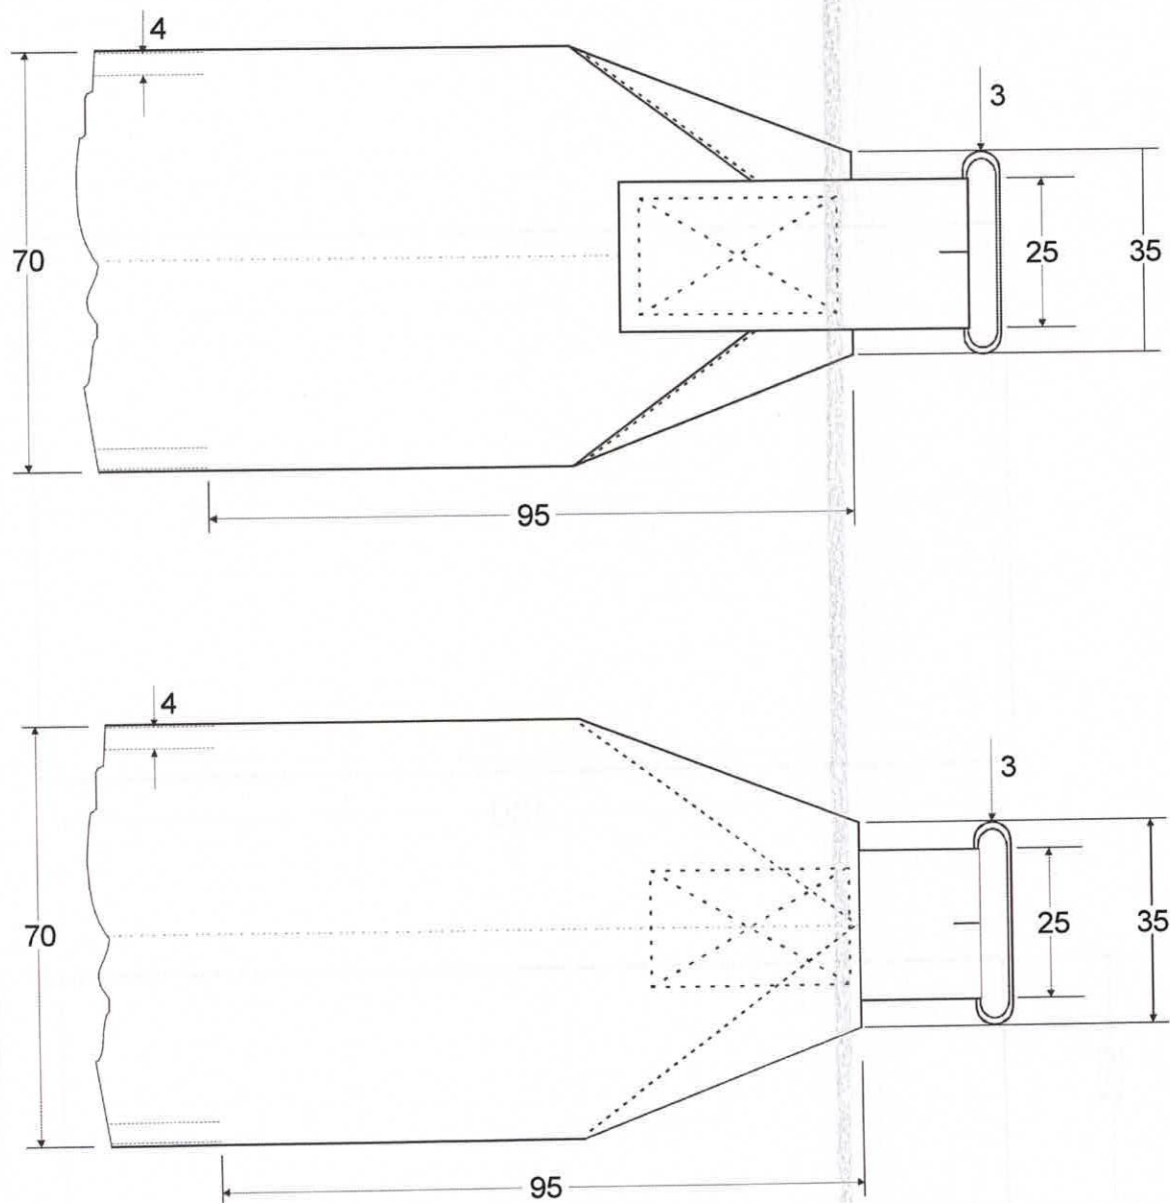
Vista da correia de fixação do suporte metálico (medidas em mm)
